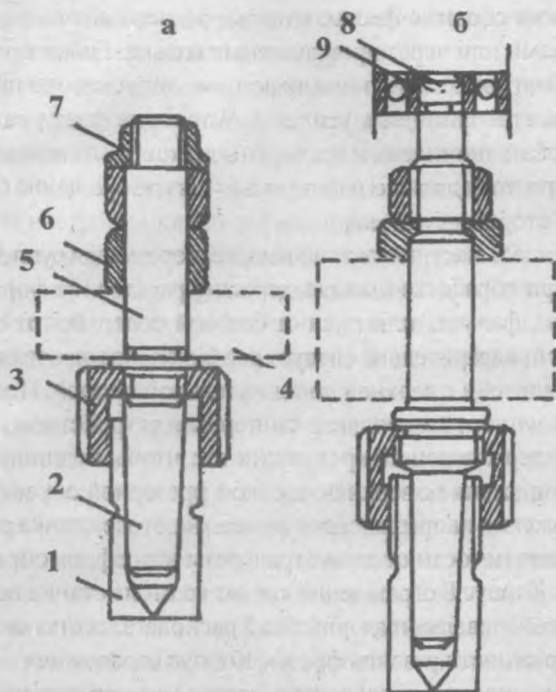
Крепление фрезы на оправке фрезерного станка:
